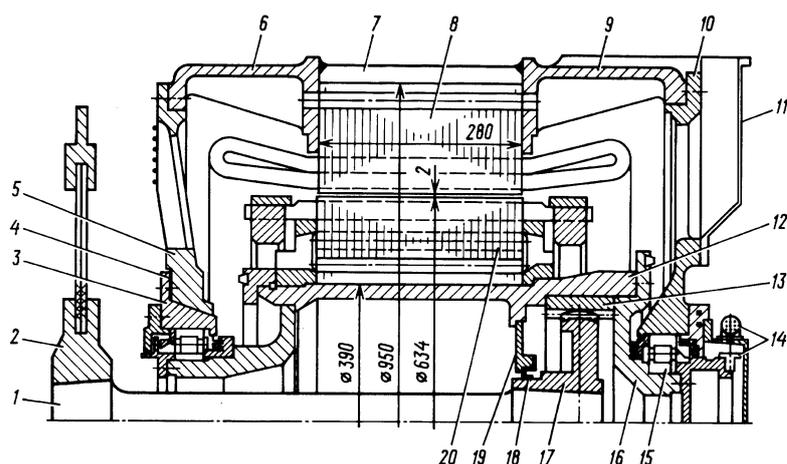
Продольный разрез АТД НТА-1200 с бескорпусной конструкцией статора:
